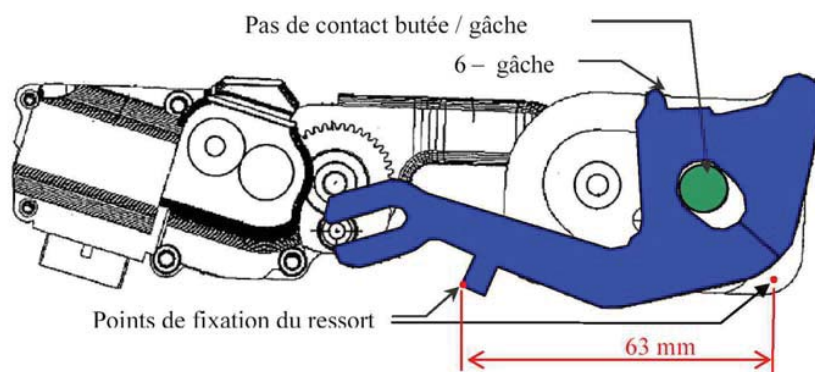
Vue d'ensemble de la gâche motorisée en position tirée - ou coffre fermé
